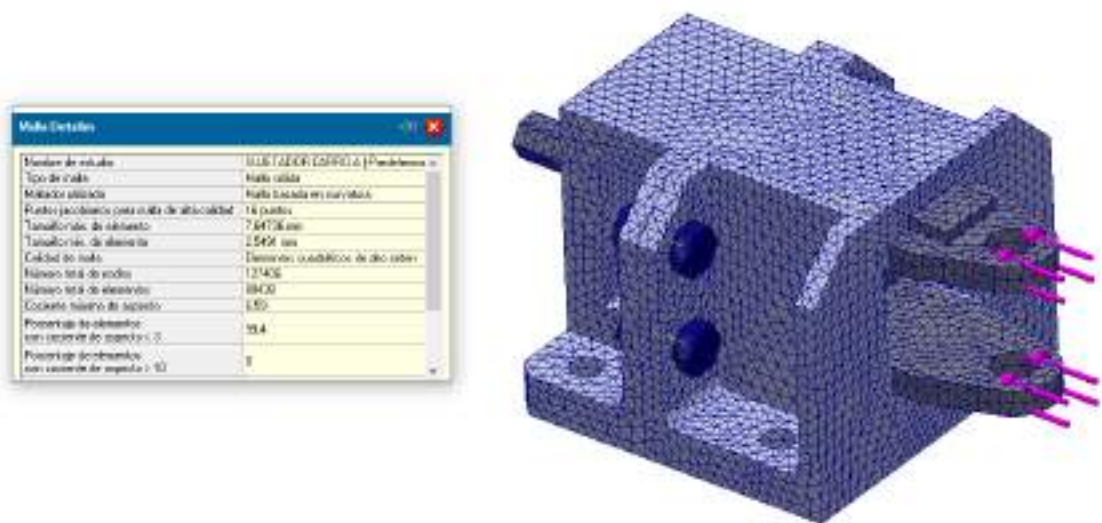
Detalles de la malla del conjunto rueda guía .
